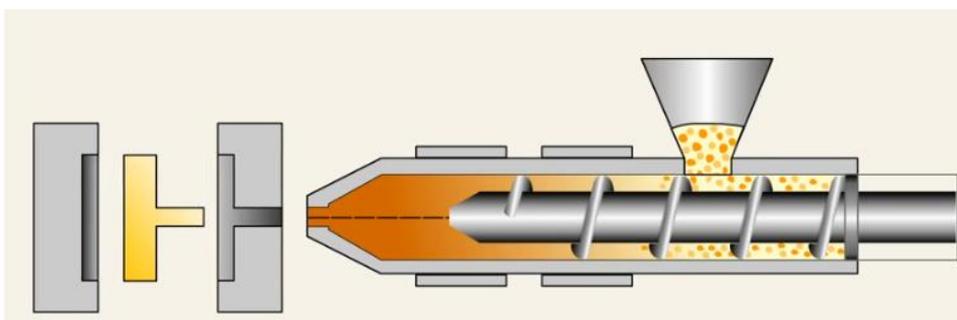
Abkühlphase und Öffnen des Werkzeuges [13]
